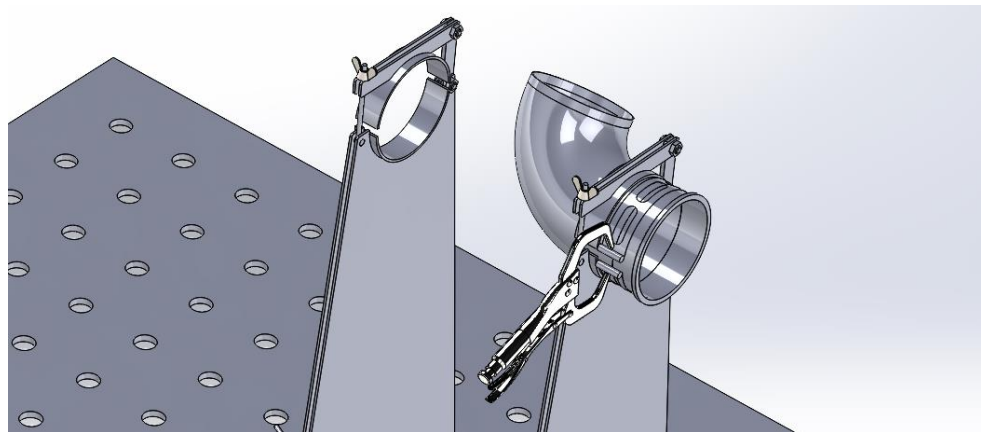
Розташування заготовок та притискачів в середині камери при зварюванні шва № 3
